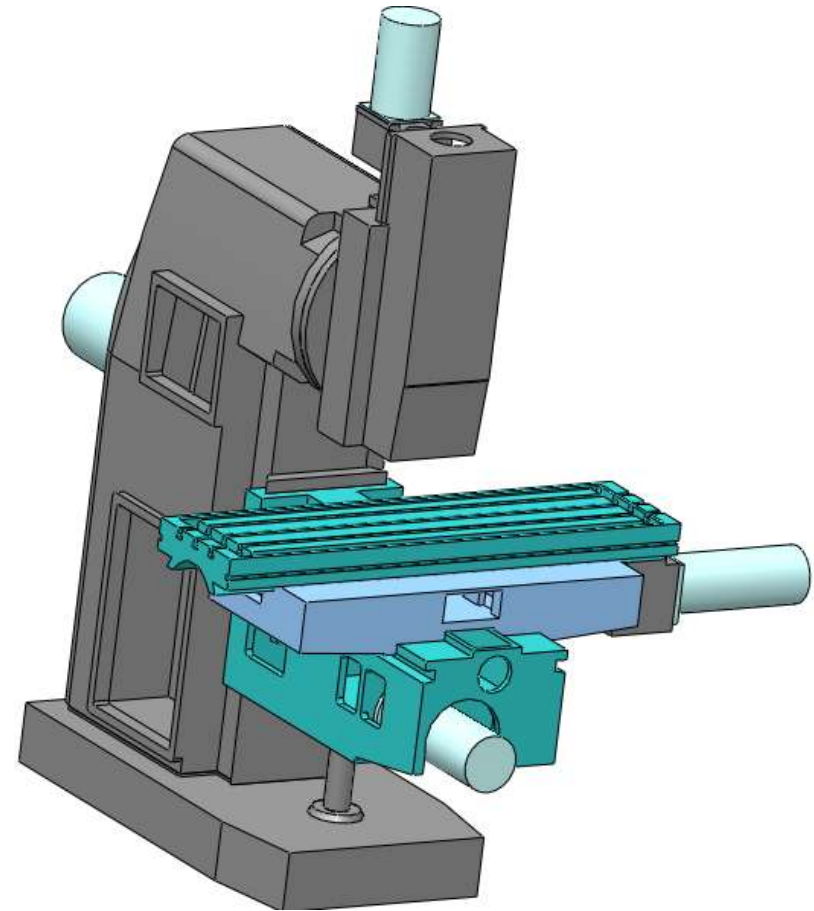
Загальний вигляд вертикально-фрезерного верстата з ЧПК 6P13Ф3
